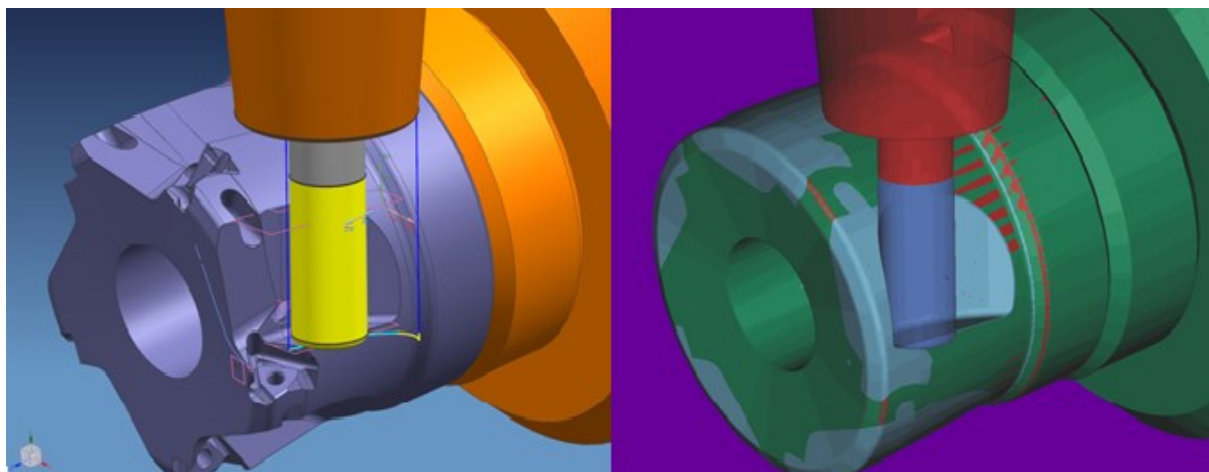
Staré naprogramování frézovacích drah při hrubování [13]
